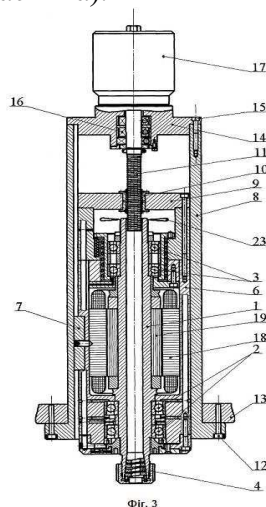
Шпindel 1, передня і задня опори 2 і 3, оправка 4, інструмент 5. піноль 6, шпонка 7, корпус 8. фланець 9, гайка 10, гвинт 11 болти 12 нерухома частина 13, перехідний фланець 14, болти 15, жорстка опора 16 кроковий електродвигун 17, статор 18, двошарова активна поверхня 19
